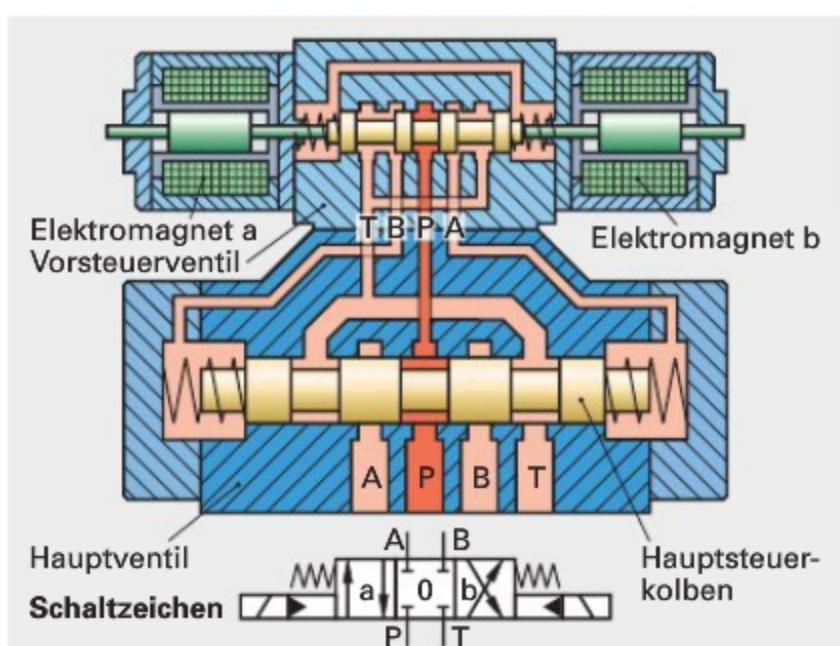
Hydraulisch vorgesteuertes Wegeventil
